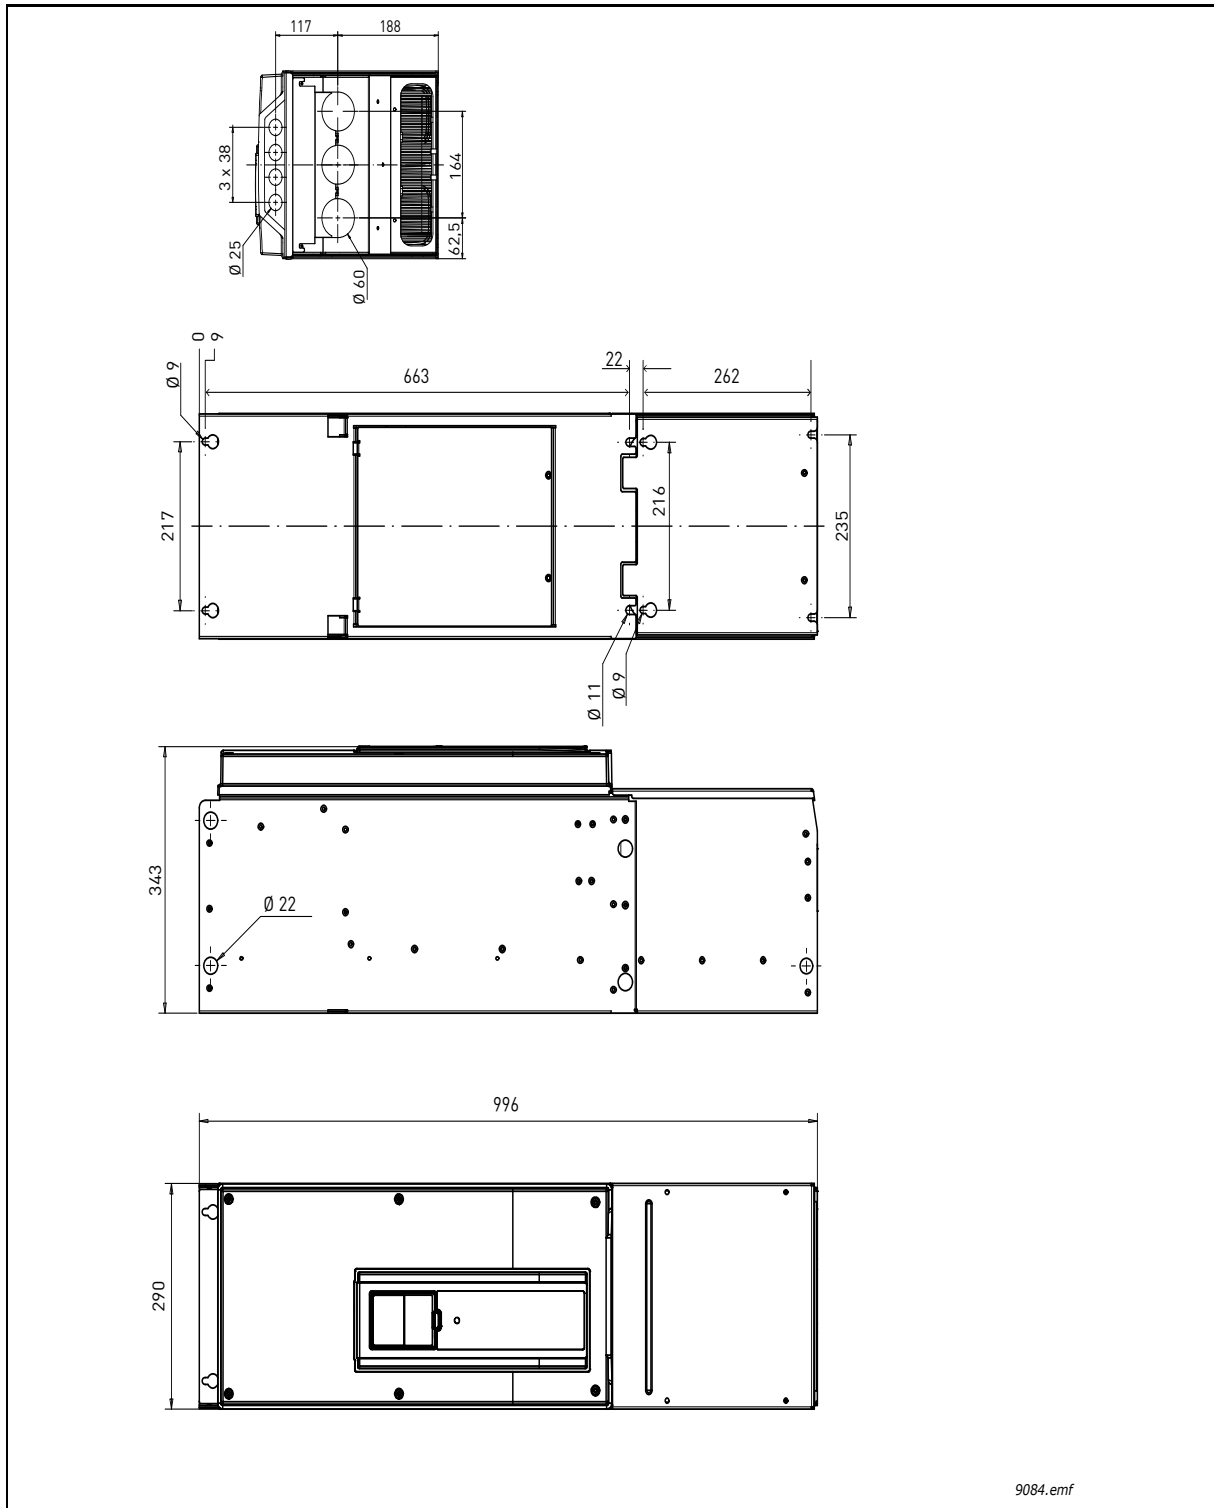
Dimensões do inversor de CA Vacon, MR8 IP21 e IP54
